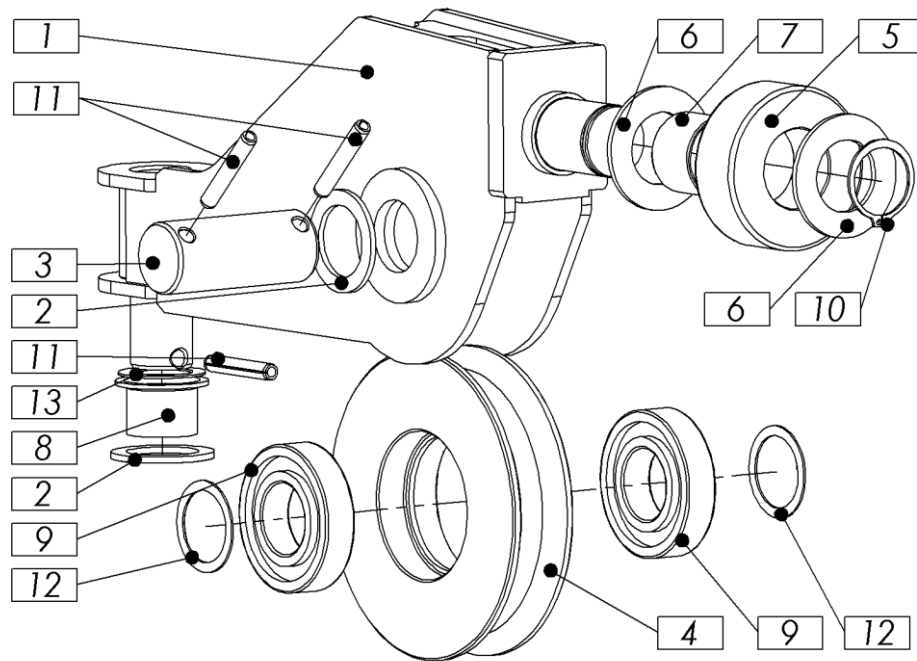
806.25.70.0 – SEILVERTEILER GESCHWEIßT
